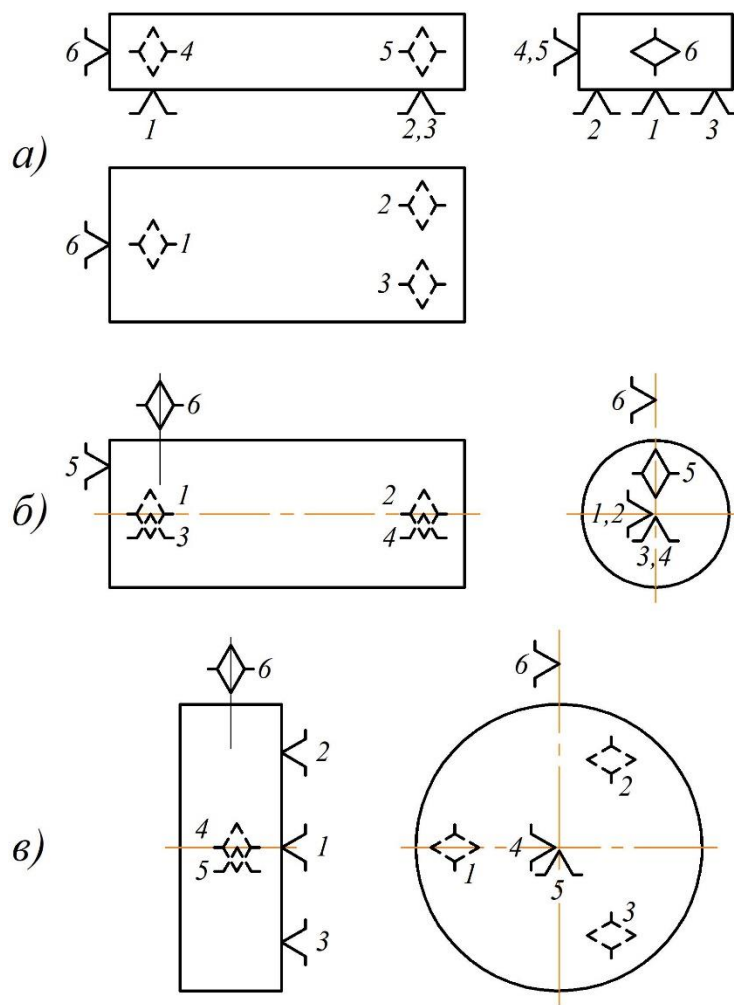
Схемы базирования: а – призматической детали; б – валика; в – диска.
